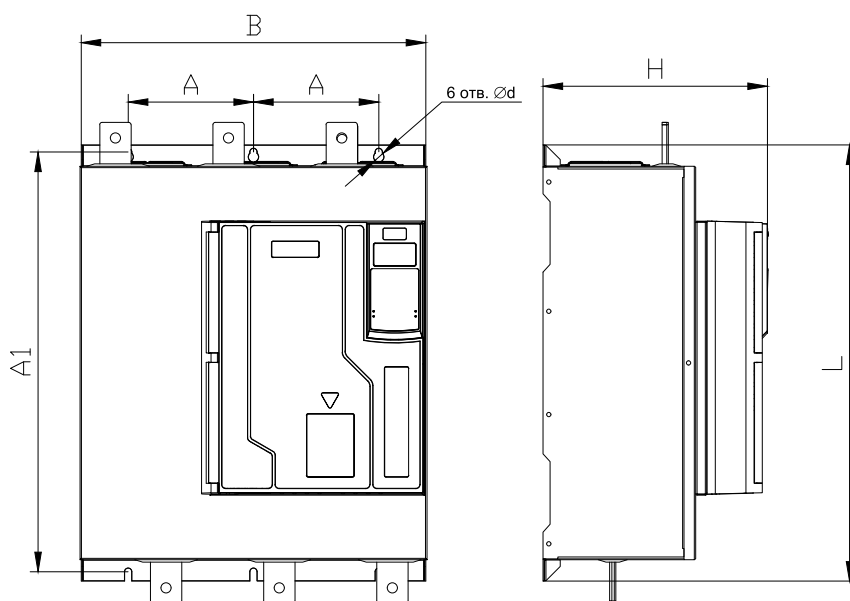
Габаритные и установочные размеры УПП, габарит 3
